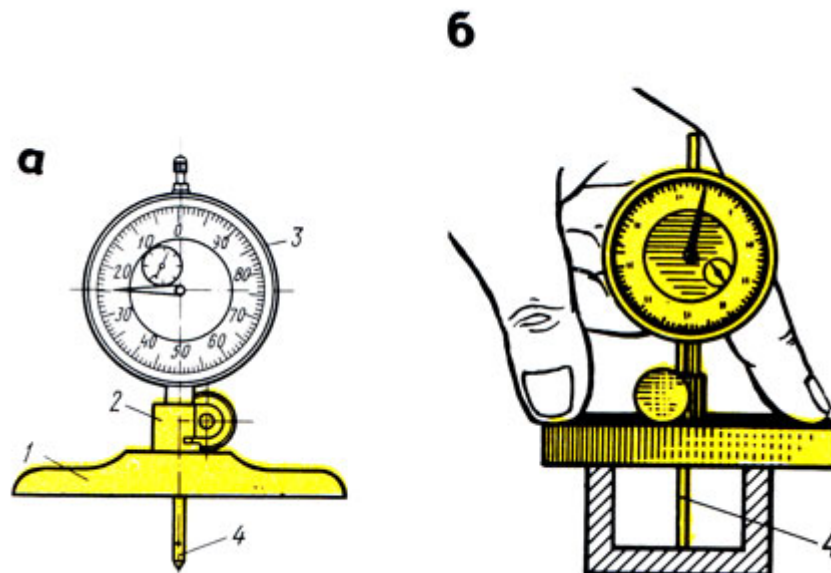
Индикаторный глубиномер: а - устройство, б - прием проверки; 1 - основание, 2 - державка, 3 - индикатор, 4 - измерительный стержень
